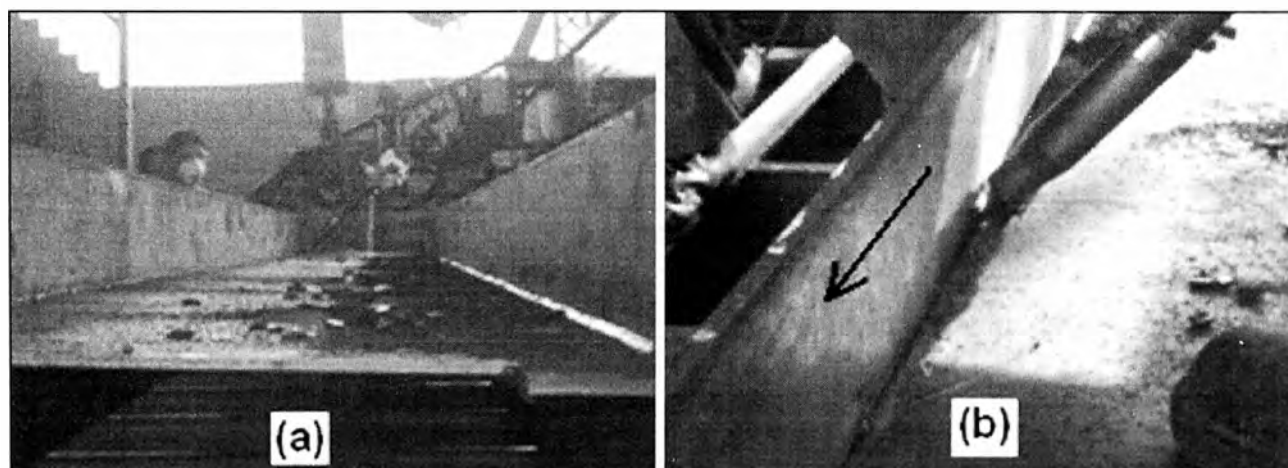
Soldadura del cuarto cordón con SAW.
